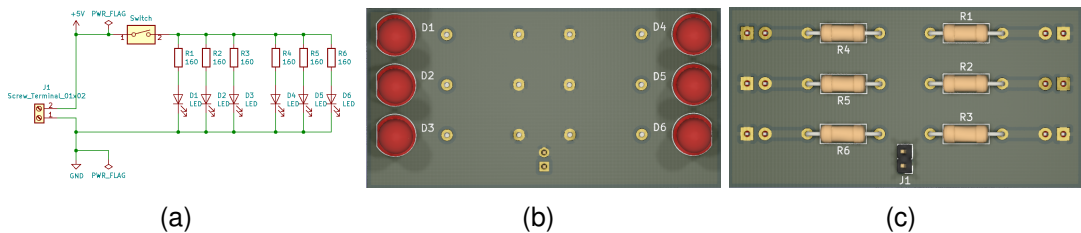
Sistema de iluminación: (a) Esquemático de la PCB, (b) PCB vista frontal, (c) PCB vista trasera
